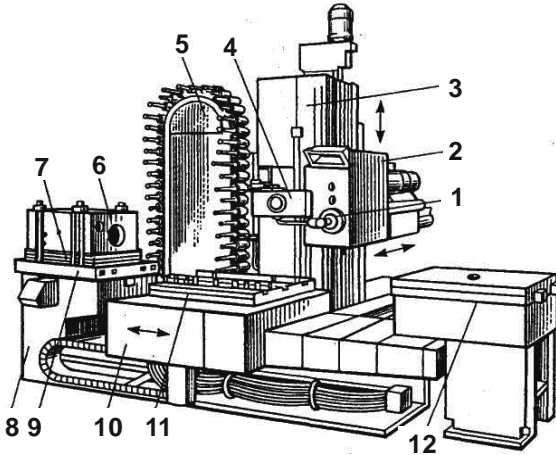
Багатоопераційний верстат із числовим програмним управлінням: 1 – шпиндель; 2 – шпиндельна бабка; 3, 8 – стояки; 4 – автооператор; 5 – магазин інструменту; 6 – заготовка; 7 – пристрій-супутник; 9, 12 – додаткові столи; 10 – нижня частина стола; 11 – верхня частина стола
